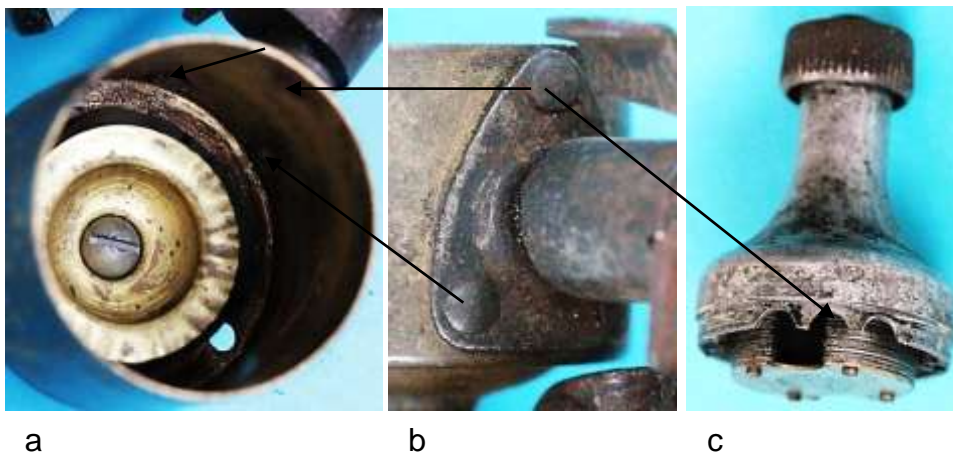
Flanschbefestigung: a) Innenansicht des Gehäusetopfes mit Nietköpfen, b) Dreieckförmiger Flansch, c) Lagerhalsfuß mit Ausnehmungen für Nietköpfe
